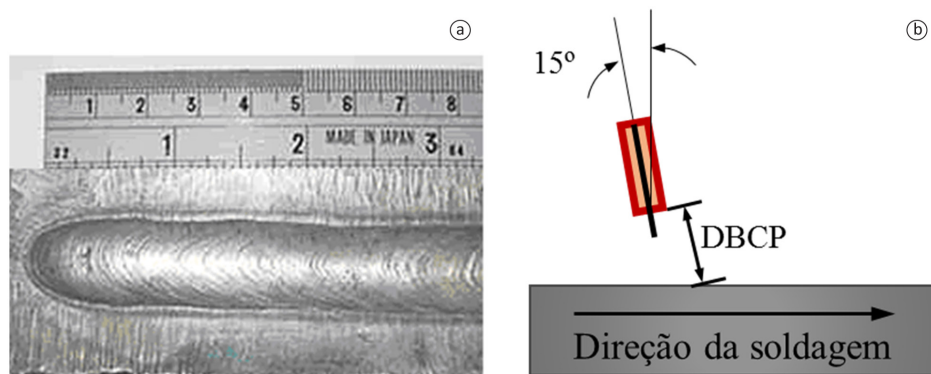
(a) Imagem do cordão de solda e (b) Técnica e procedimento de soldagem.
